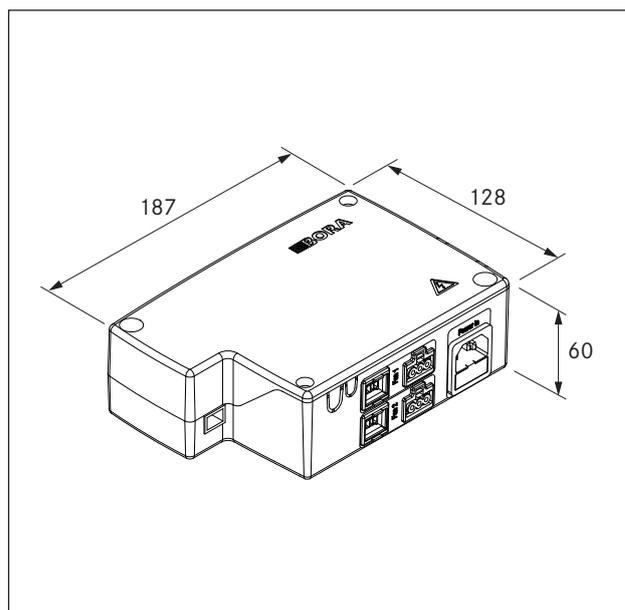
Dimensioni di montaggio unità di controllo Universal
